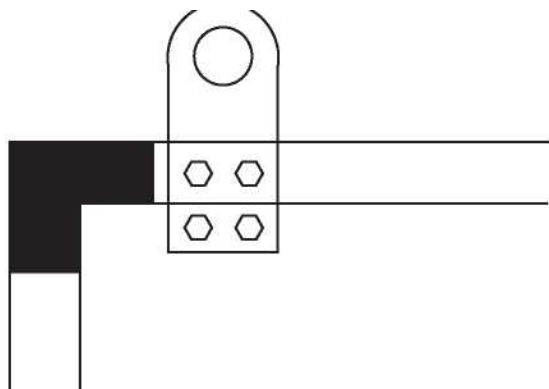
Транспортировочные проушины -крышки, торцевая стенка и разделительное соединение
